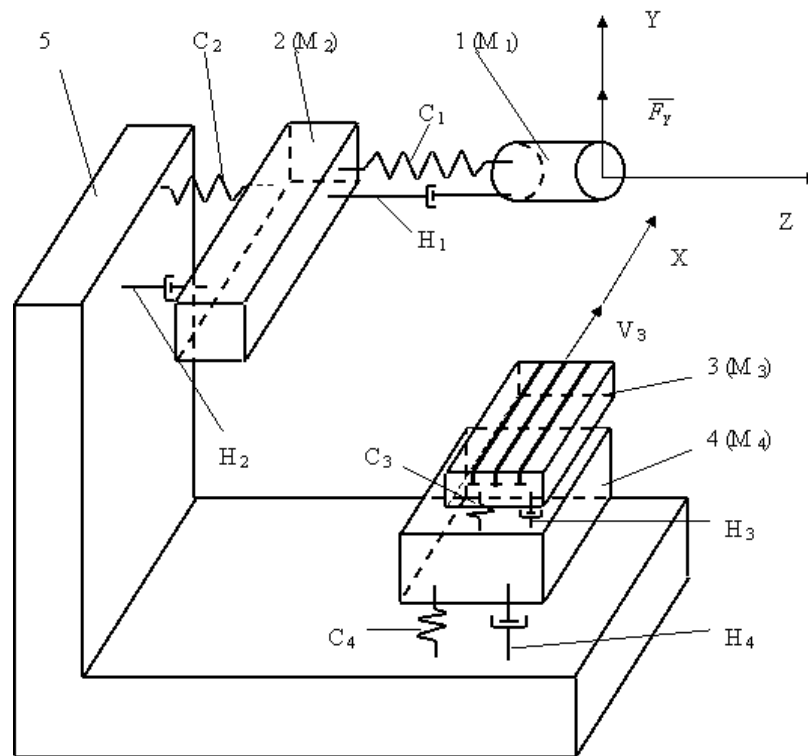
Розрахункова схема пружної системи верстата,
